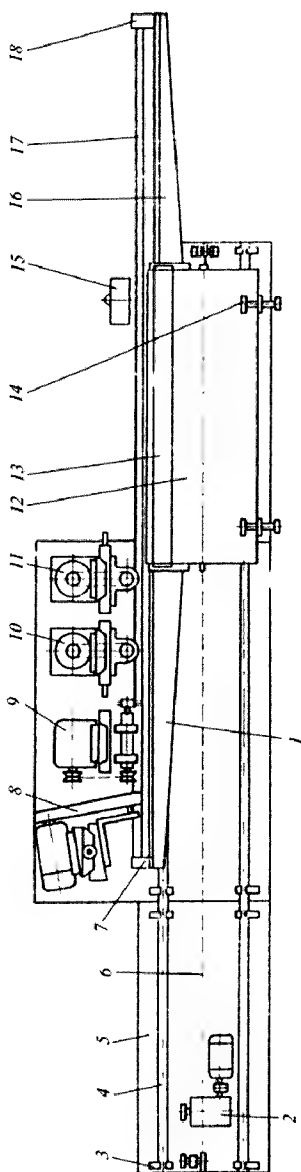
Схема станка модели 3Ш-4 для зачистки кромок шлифовальной шкурки.
